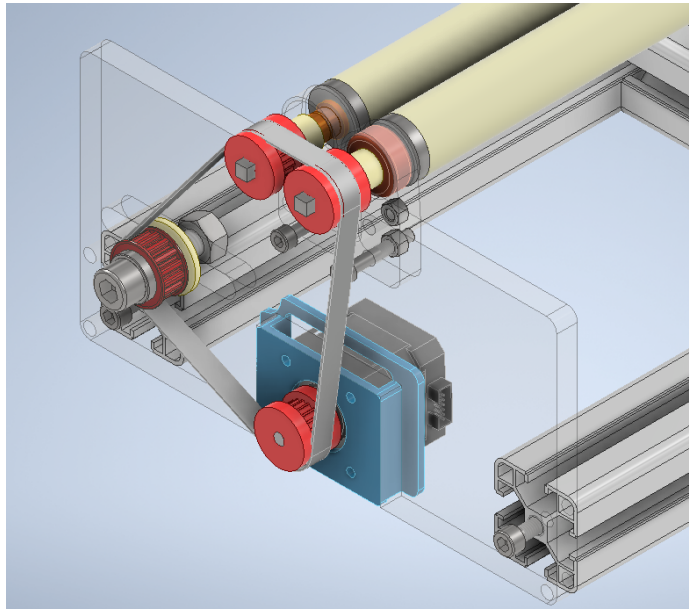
Modelado en 3D del lado de accionamiento del dispositivo.
